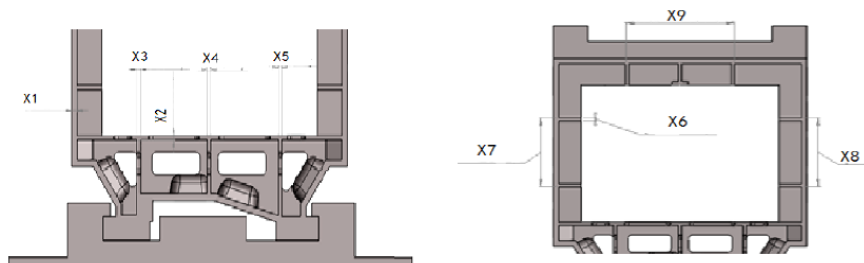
Rám stroje s obdélníkovými a trojúhelníkovými prvky (9)
